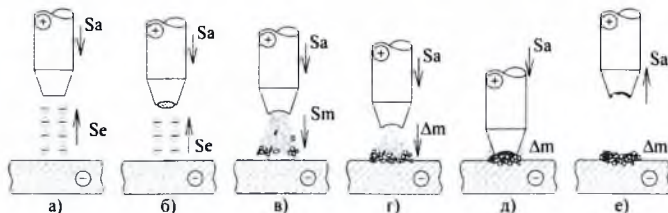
Схема процесса ЭИЛ: а - образование канала сквозной проводимости; б - образование капли расплавленного металла; в - взрыв расплавленной капли металла; г - прилипание и внедрение частиц на поверхности катода; д - “проковывание” покрытия; е - движение анода от поверхности катода
